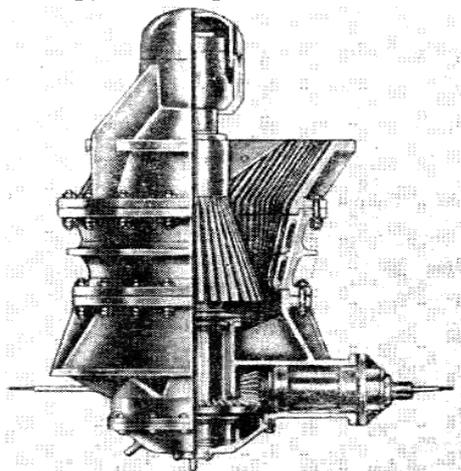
Общий вид щеково-конусной дробилки «Эш-Верке»
